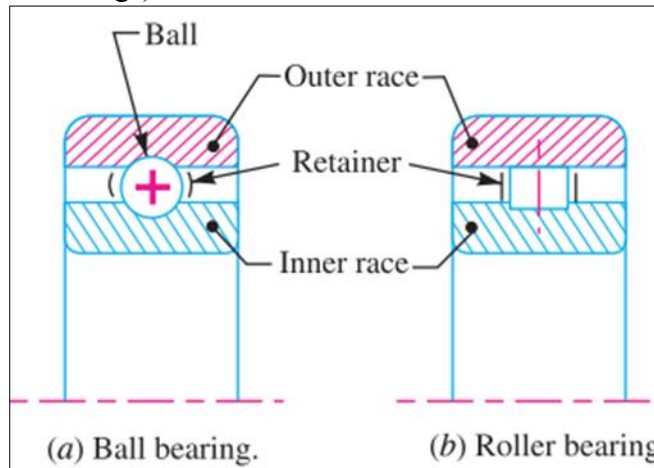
बॉल व रोलर बेअरिंग्स (Ball and Roller Bearings)
